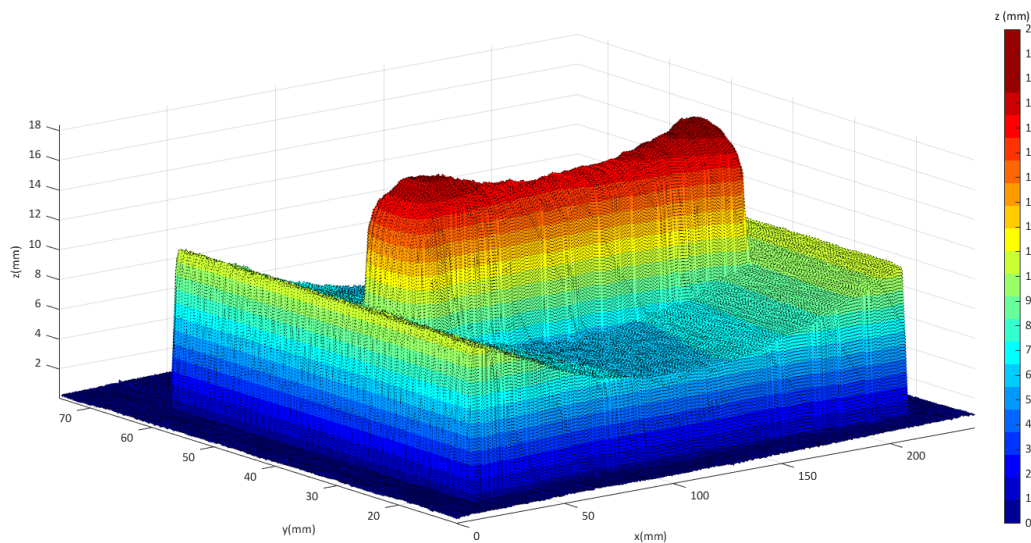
VUE TRIDIMENSIONNELLE DE L'ESSAI N°4
